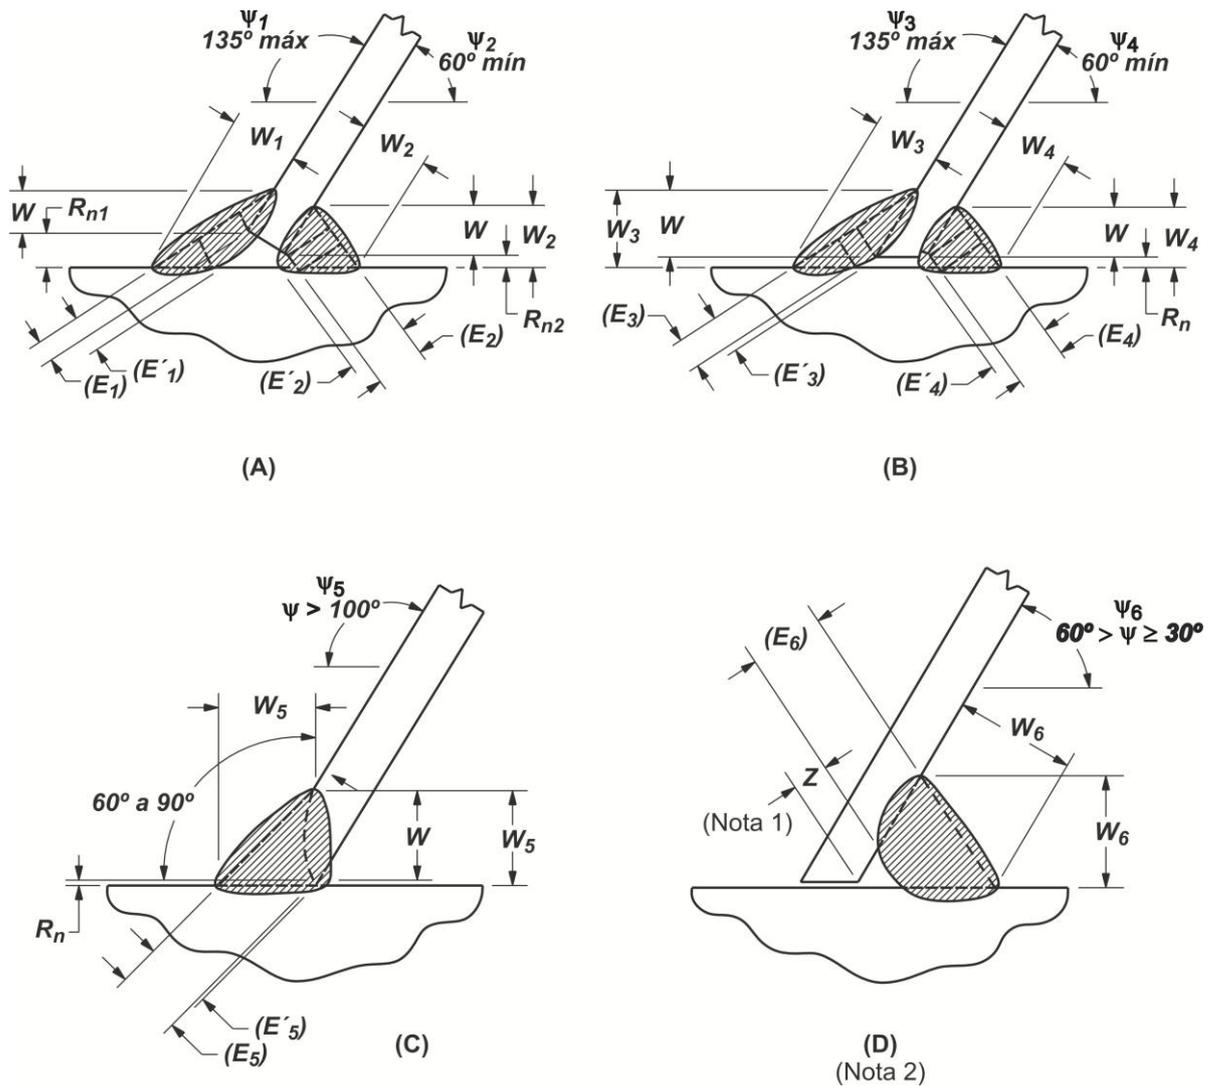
Detalles de juntas precalificadas para soldaduras con bisel y JPC en uniones tubulares T, K e Y – Perfiles de soldadura con filete de terminación para espesor intermedio.
